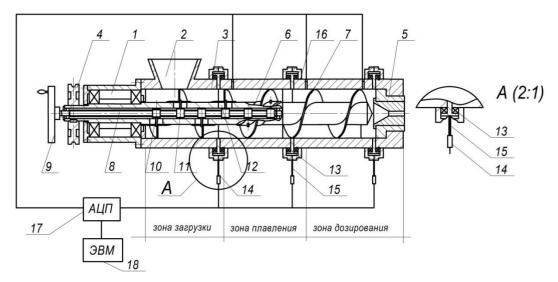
Схема установки с автоматическим контуром управления для экструдирования кормовых продуктов: 1 — подшипниковый узел, 2 — загрузочная воронка, 3 — разъёмные корпуса шнековой камеры, 4 — привод, 5 — формующая головка, 6 — шнек, 7 — витки шнека, 8 — резьбовой вал, 9 — приводной механизм, 10 — втулки с установленными пальцами 11, 12 — направляющие, выполненные в теле шнека, 13 — цилиндрическая вставка, 14 — тензодатчики, 15 — гибкие элементы, 16 —датчики температуры, 17 — аналогоцифровой преобразователь, 18 — компьютер.
